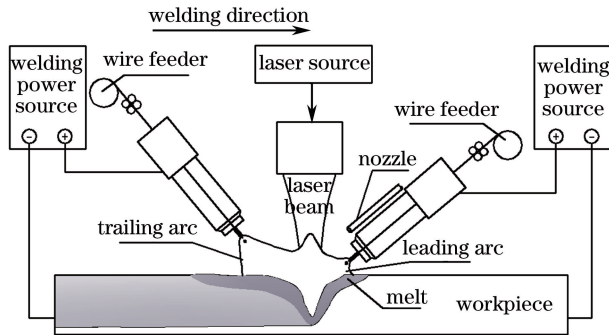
激光-双 MIG 电弧复合焊接装置
